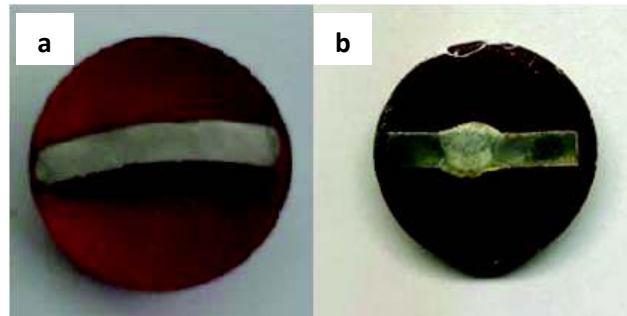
a) Probeta del material base, b) Probeta de la soldadura.
